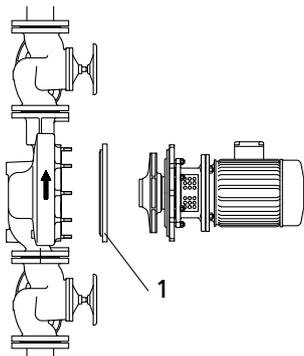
Montaggio orizzontale con flangia cieca (1 = flangia cieca, accessorio)
